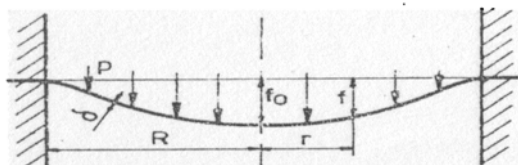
Schemă pentru dimensionarea unei membrane metalice
